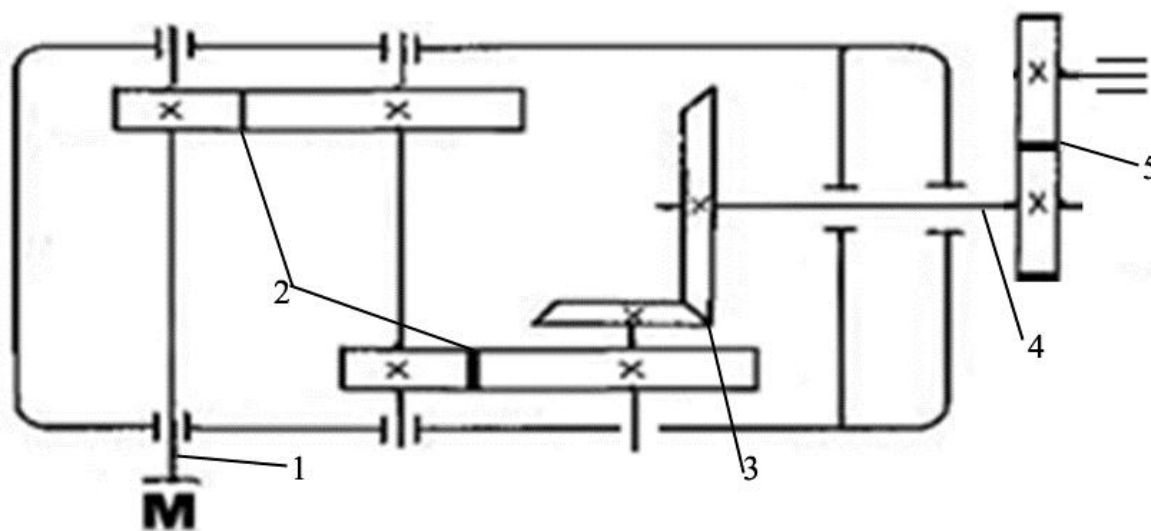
Кинематическая схема механизма: 1-Входной вал редуктора; 2-Прямозубая передача, колеса зацепления; 3-Угловая передача; 4-Выходной вал редуктора; 5-Прижимной механизм подачи проволоки
